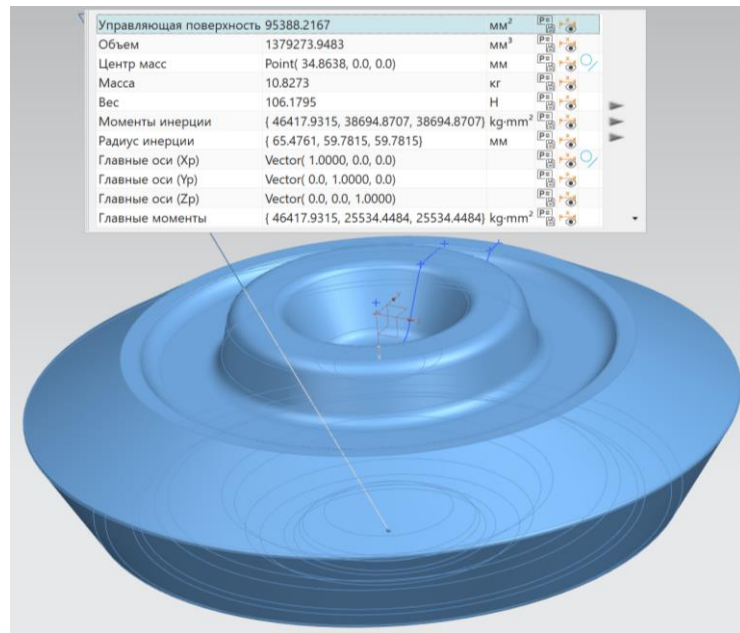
Модель штампованной заготовки на КГШП
